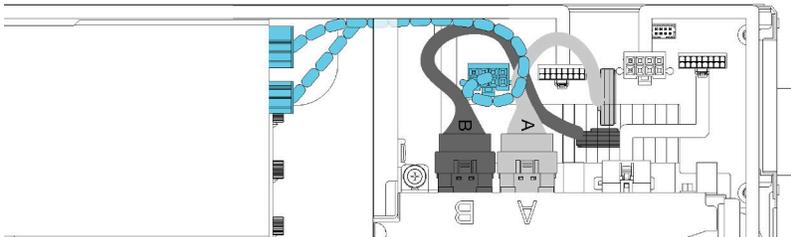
Roteamento do PCIe#1-A, PCIe#2-B e do cabo de energia auxiliar da placa riser frontal
